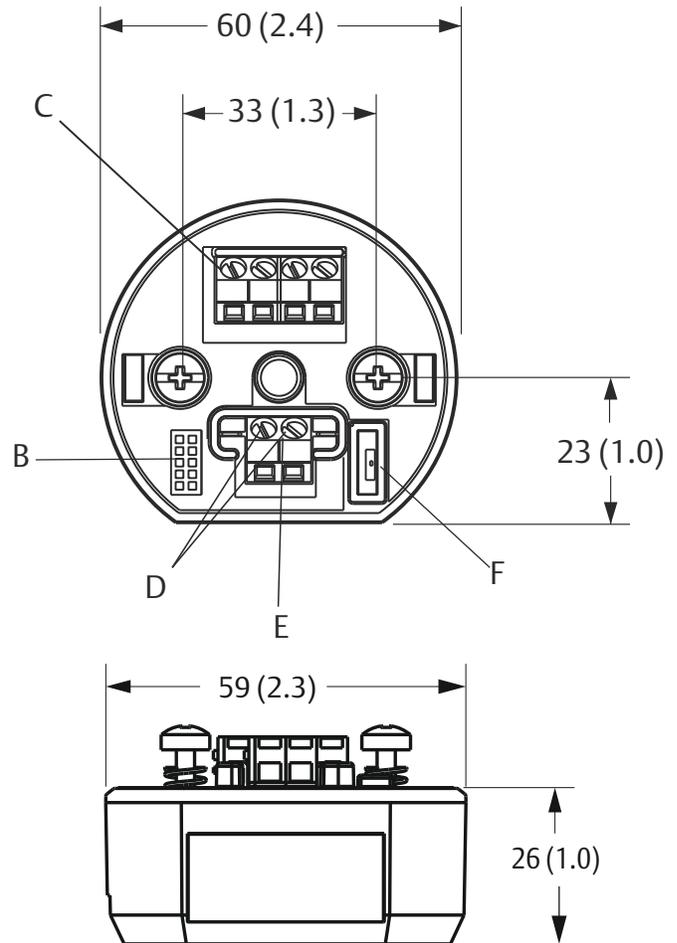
Rosemount 644H (DIN A Kopfmontage)
